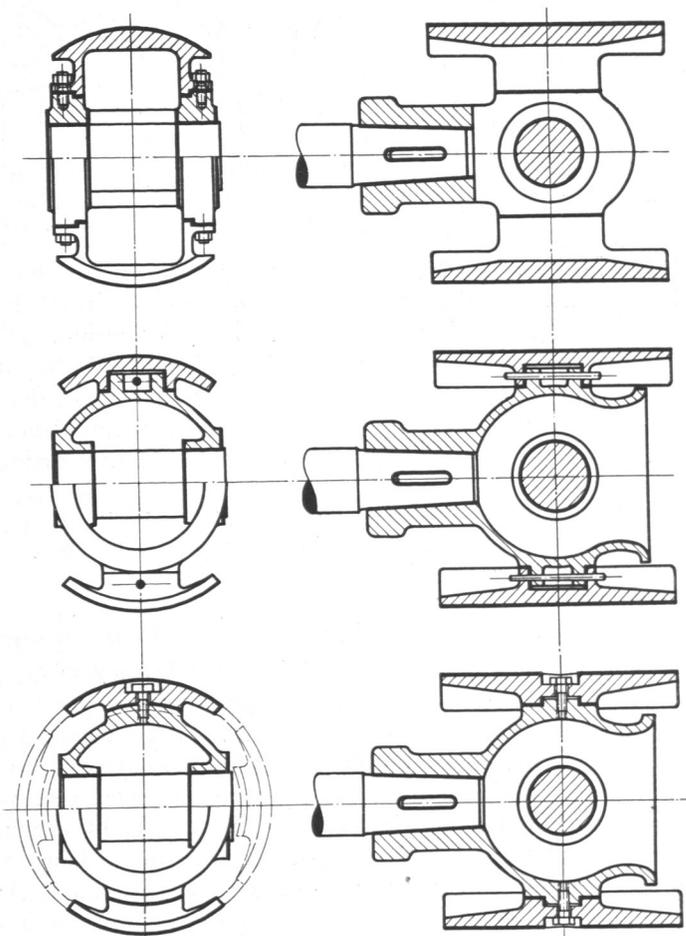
222. Verschiedene Kreuzkopfformen und ihre Bearbeitung.
